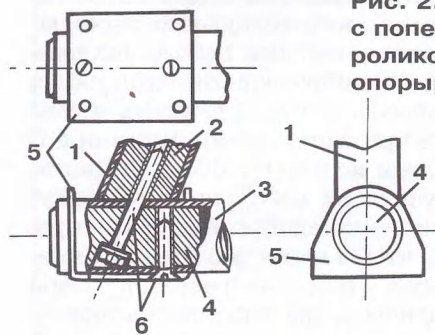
Соединительный узел опоры с поперечиной и кронштейном для роликов: 1 — опора; 2 — нижняя втулка опоры; 3 — поперечина; 4 — втулка поперечины; 5 — кронштейн; 6 — крепежные винты.
